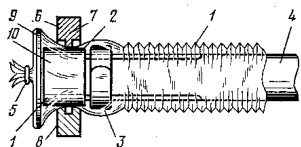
Аппарат для изготовления колбас с выровненными концами.
